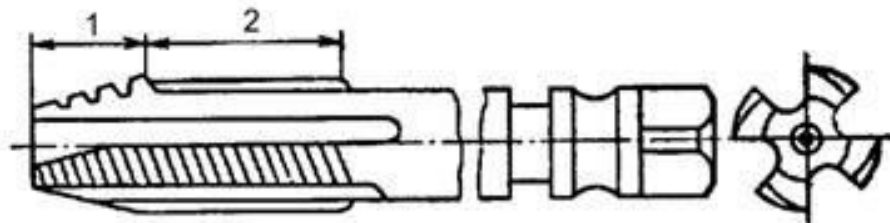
Конструкція мітчика: 1 ріжуча (огорожуюча) частина; 2 - калібруюча частина
